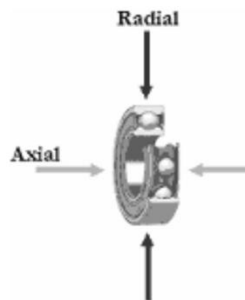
Cargas axiales y radiales en un rodamiento [20].
